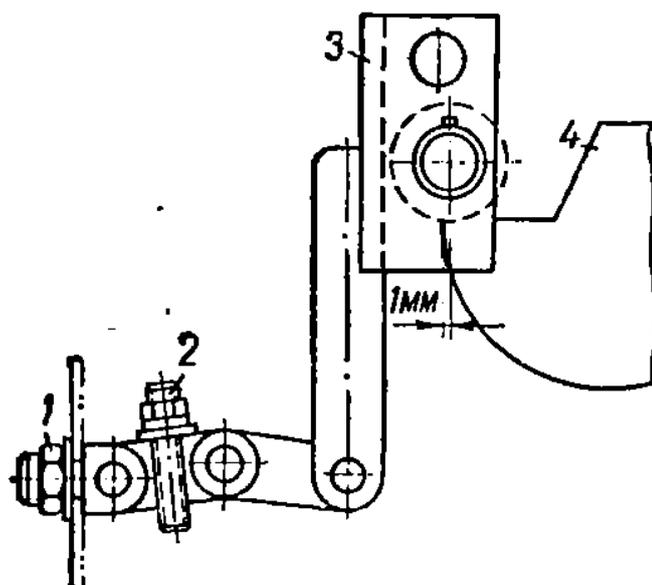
Узел для регулировки механизма включения привода типа ППМ-10: 1,2 - гайки; 3 - удерживающий механизм; 4 - рычаг
